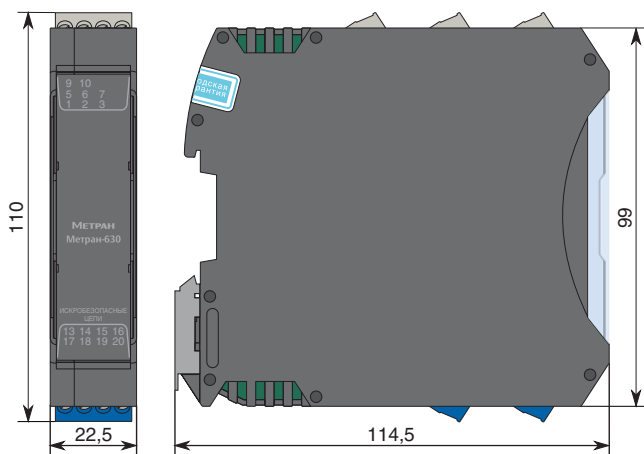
Габаритные размеры барьера в корпусе шириной 22,5 мм с разъемами с винтовыми клеммниками
